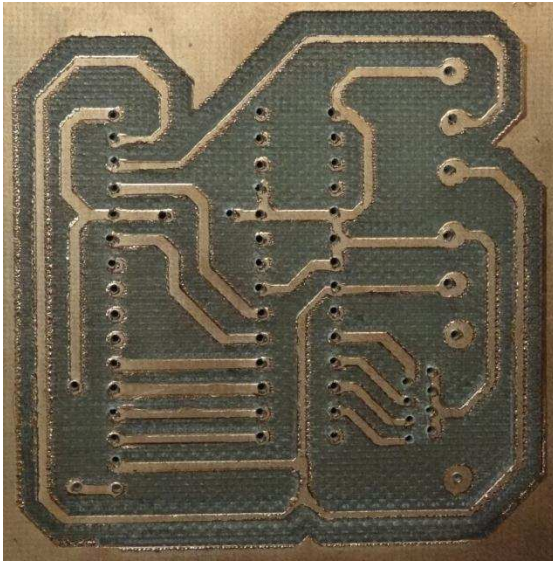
PCB con fresa cónica, desbastado 100%, broca fina
